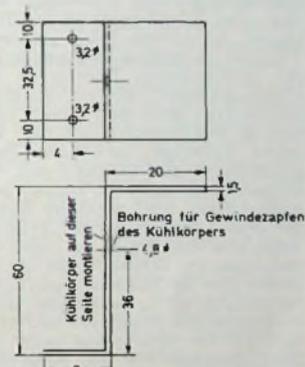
Kühlblech für T5 auf der Printplatte NG (Material: Al, 1,5 mm)
